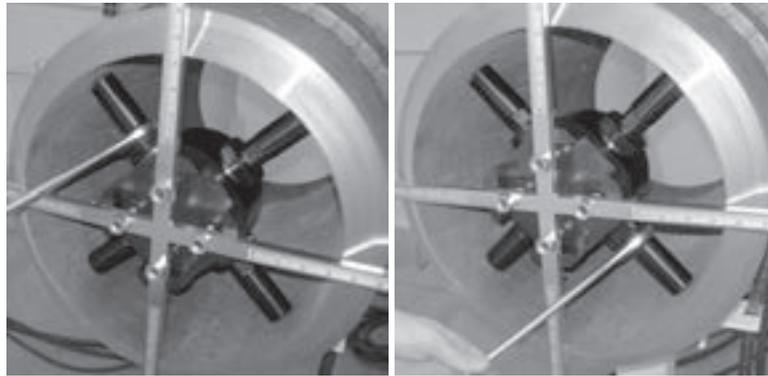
Ajuste alternadamente las patas opuestas para centrar el plato en el tubo.
